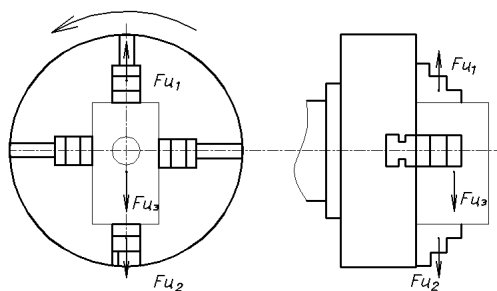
Действие центробежной силы при растачивании корпуса редуктора
